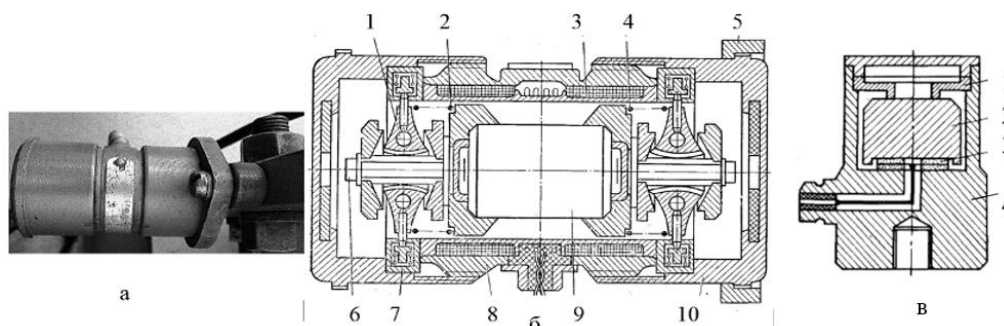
Внешний вид (а) и конструктивная схема (б) датчика вибрации МВ-25 (1 – сектор; 2,4 – пружина; 3 – катушка; 5 – фланец; 6 – крышка; 7 – постоянный магнит; 8 – корпус; 9 – подшипник; 10 – винт), схема пьезоэлектрического вибропреобразователя [4] (в) (1 – пружина, 2 – инерционная масса, 3 – пьезокерамическая пластина, 4 – корпус)
